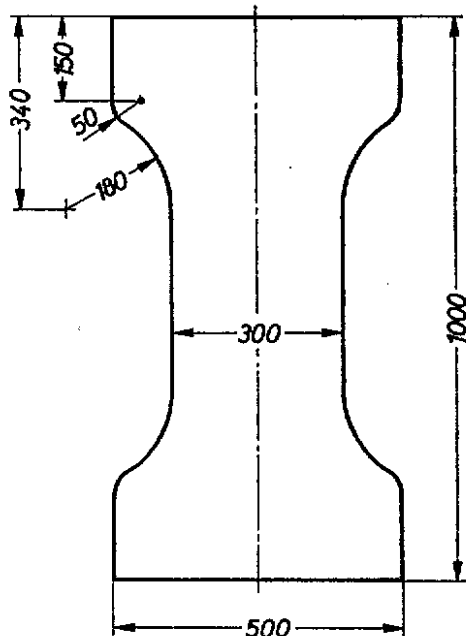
Probekörper für die Prüfung der Zugfestigkeit (zugleich Schablone zum Zuschneiden).
